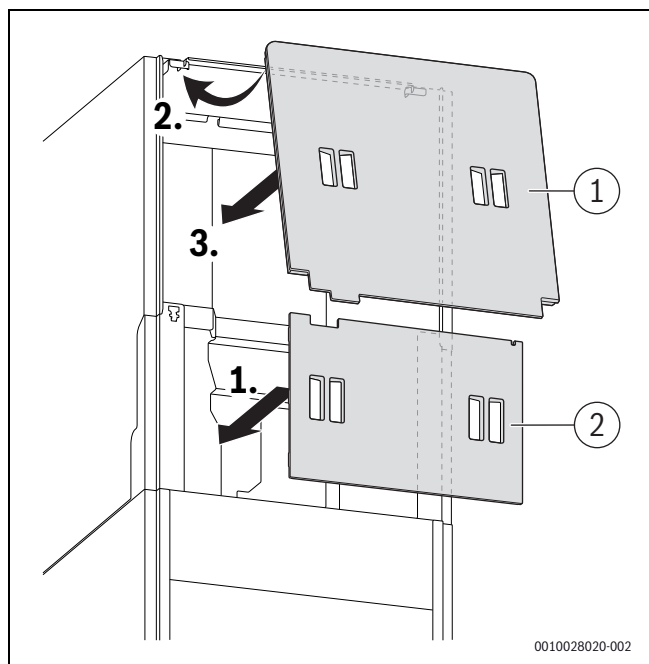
Установка дополнительного оборудования SF 13 с обратной стороны котла
